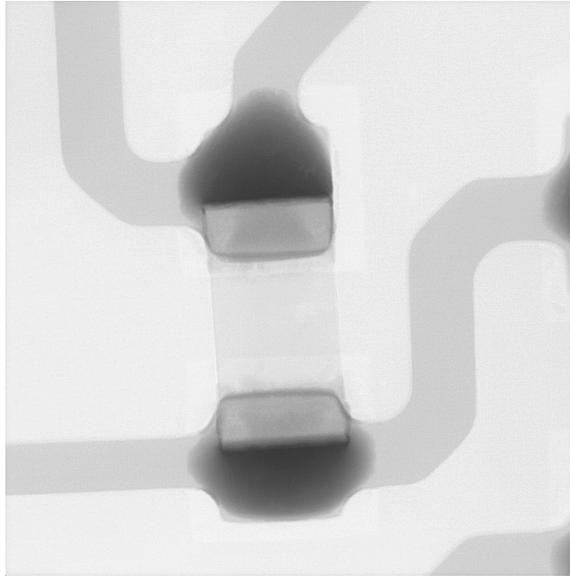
La soldadura no presenta ningún defecto en las uniones soldadas.
